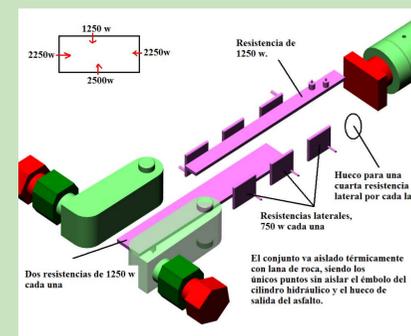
Detalle del sistema de calefacción del dispositivo extrusor.
